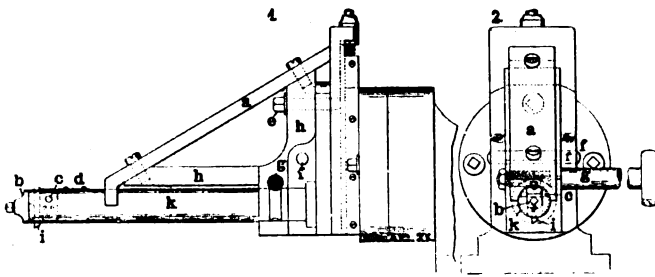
Z. A.: Interessante amerikanische Werkzeuge, Werkzeughalter etc.
